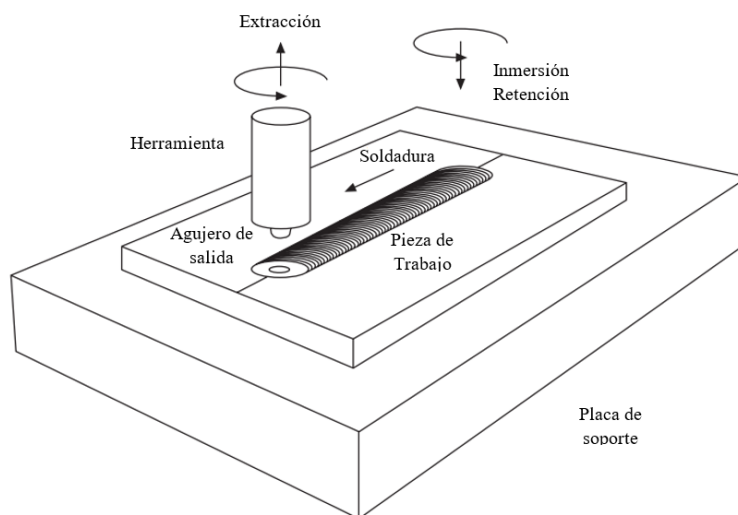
Esquema de la configuración de la FSW con la pieza de trabajo, la herramienta y la placa de respaldo, así como el movimiento de la herramienta durante los periodos de inmersión, retención, soldadura y extracción [18].
